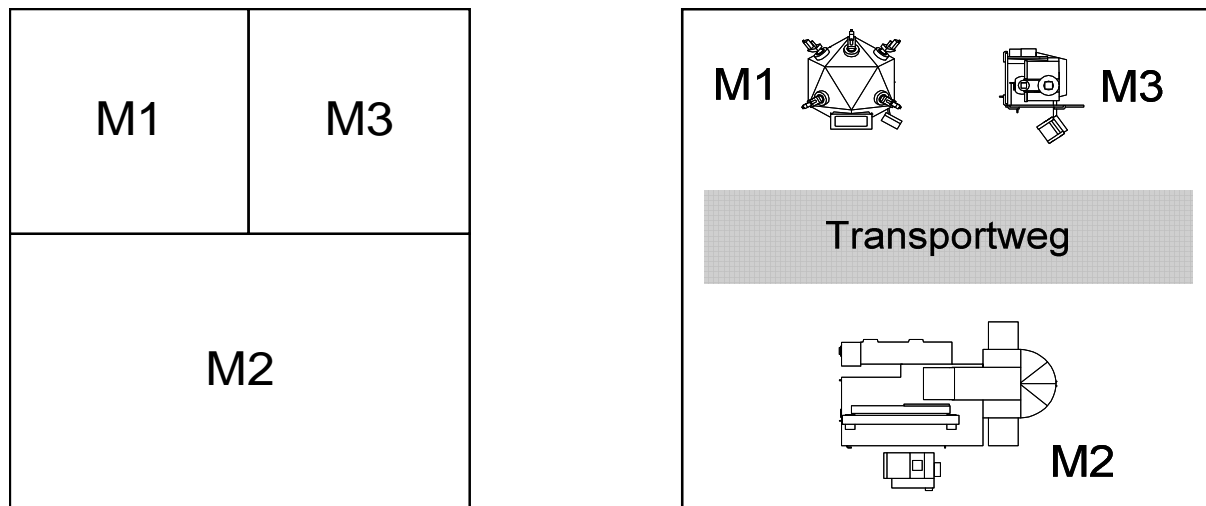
Blocklayout (links) und 2D-Layoutzeichnung (rechts)
